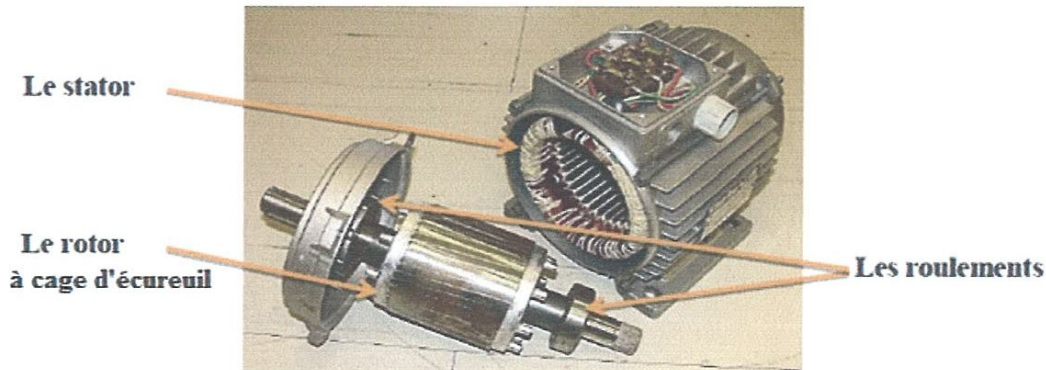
Stator, rotor à cage et les roulements de moteur asynchrone
